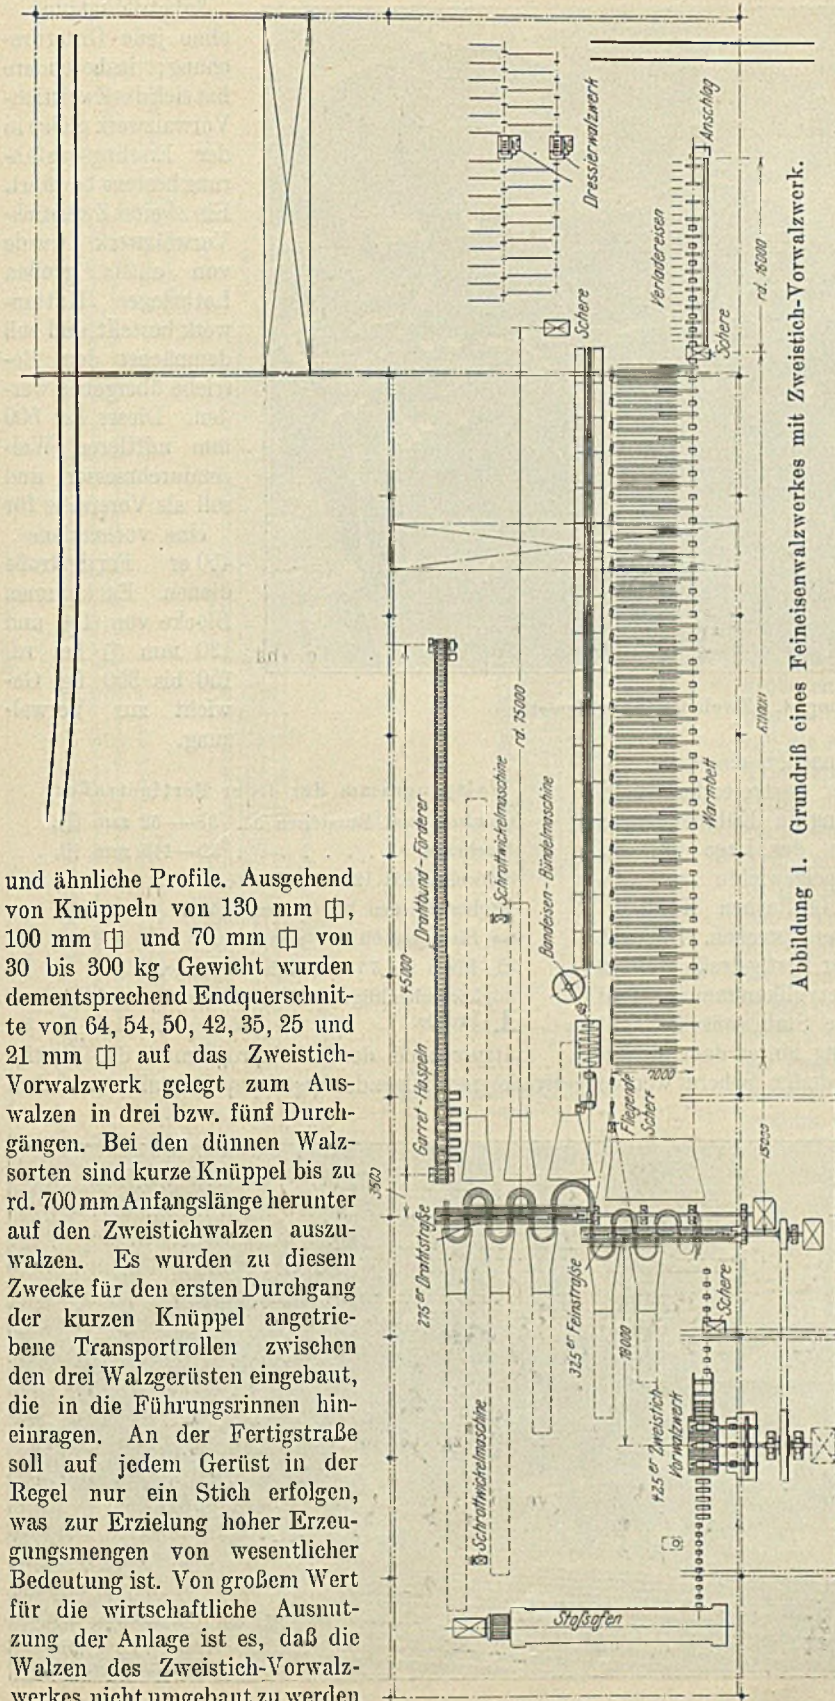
Grundriß eines Feinisenwalzwerkes mit Zweistich-Vorwalzwerk.
